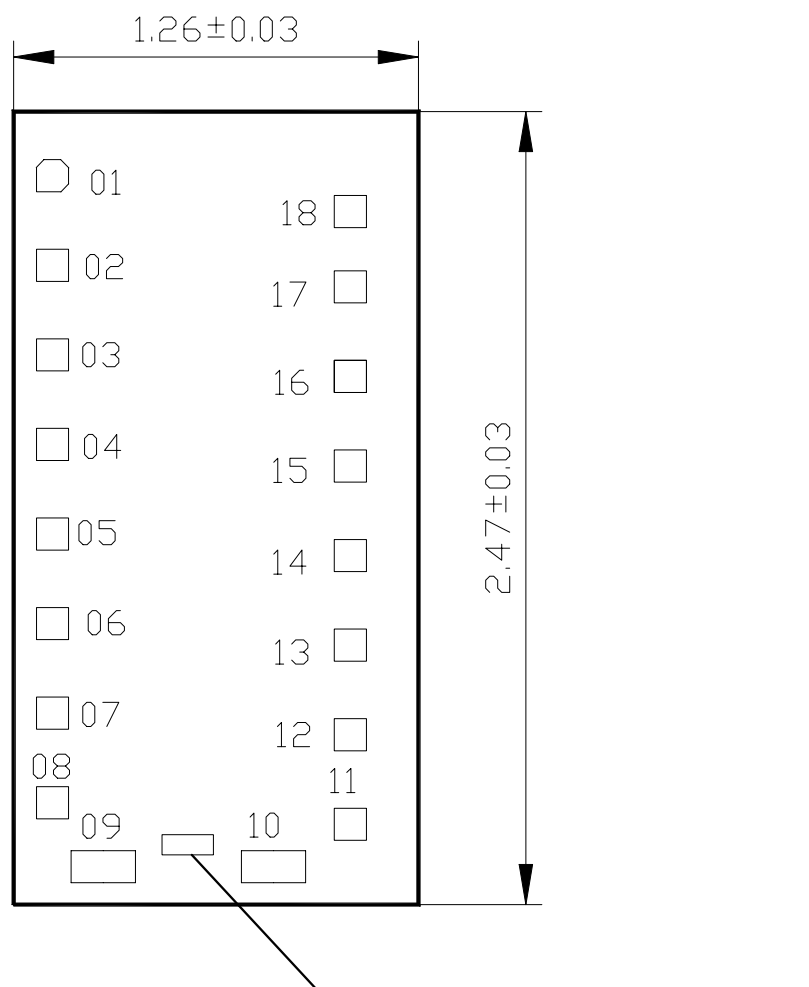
Габаритный чертеж корпуса MS-001AC
